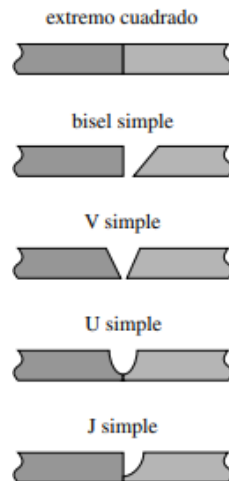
Preparación de la junta para ensambles soldados [28].
